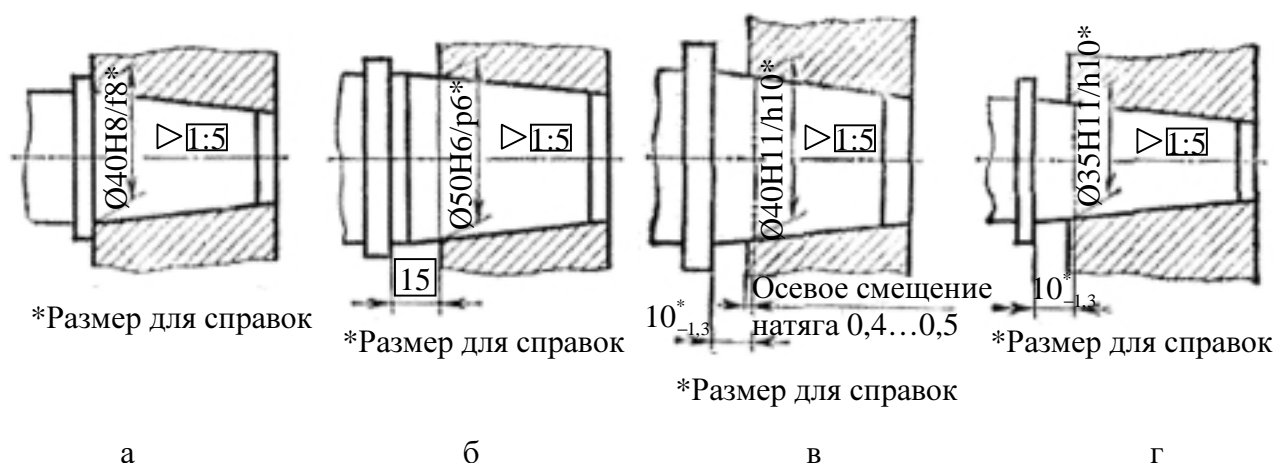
Варианты обозначения размеров и посадок на чертежах конических соединений
